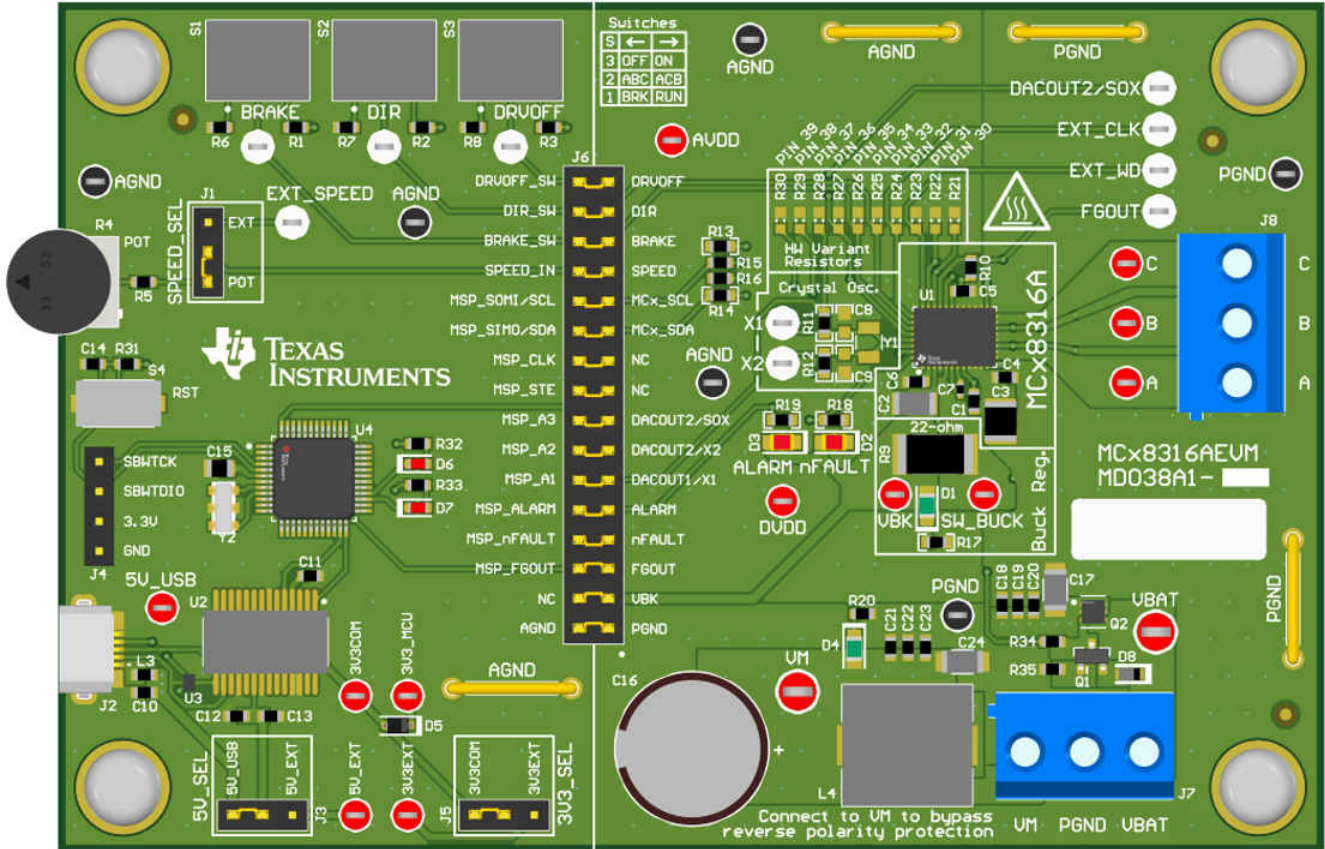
MCT8316AEVM 印刷电路板 (PCB - 顶视图)
